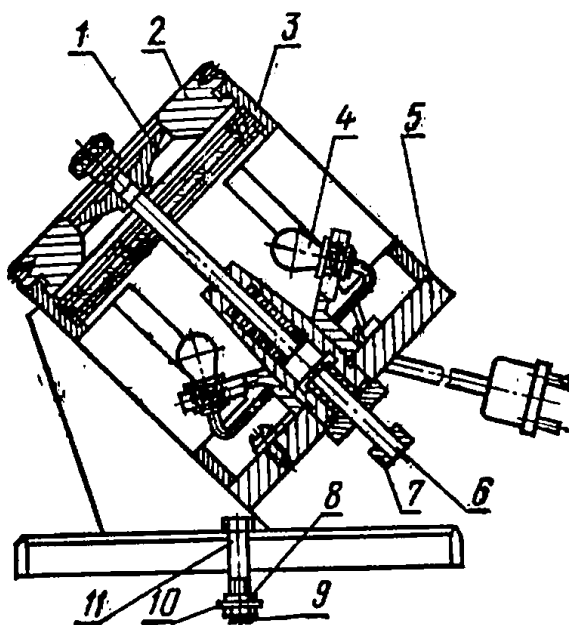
Приспособление для проверки наружного диаметра пальцев:
